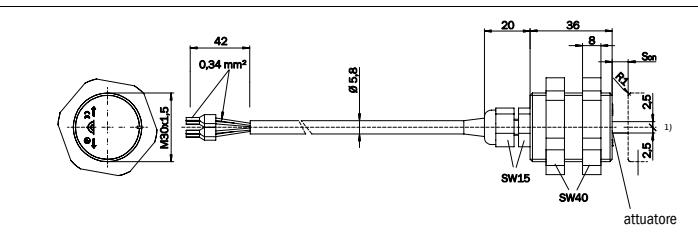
disegno quotato della testa di lettura degli interruttori di sicurezza ad azionamento magnetico RE31-DA..
